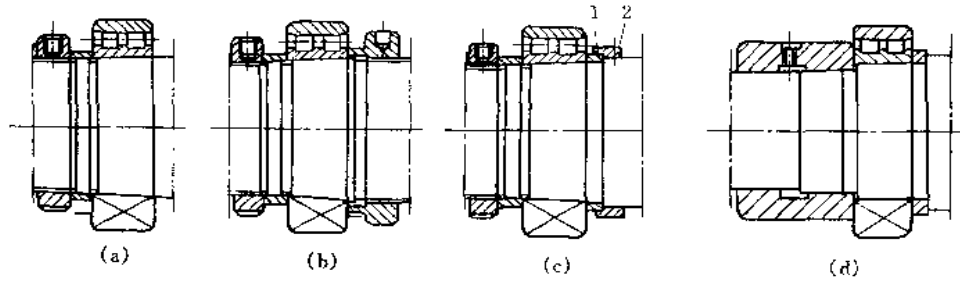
圆锥孔双列圆柱滚子轴承的调整
